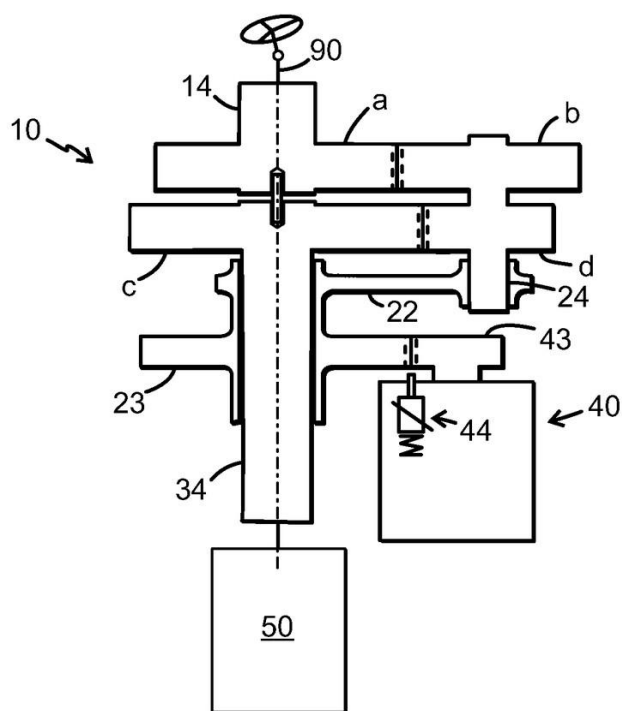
Зубчатая передача колеса рулевого управления
